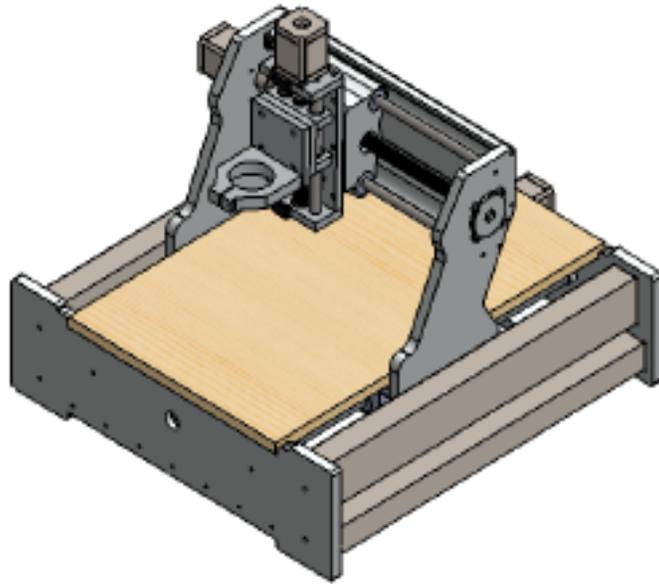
Diseño mecánico completo de la máquina CNC, modelado en SW.
